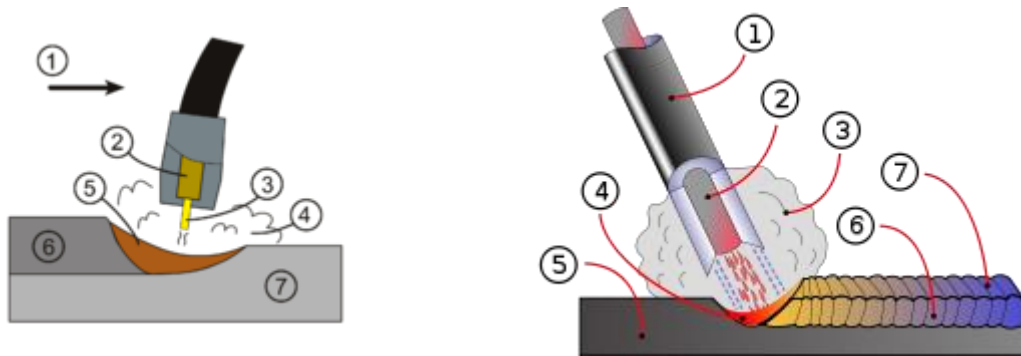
Загальна схема зварювання в захисному газі
